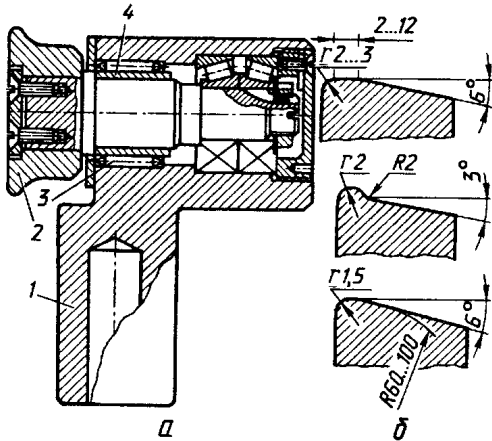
Стандартна накатна роликова головка: а - креслення головки; б - форми профілю накатних роликів; 1 - корпус; 2 - ролик;
